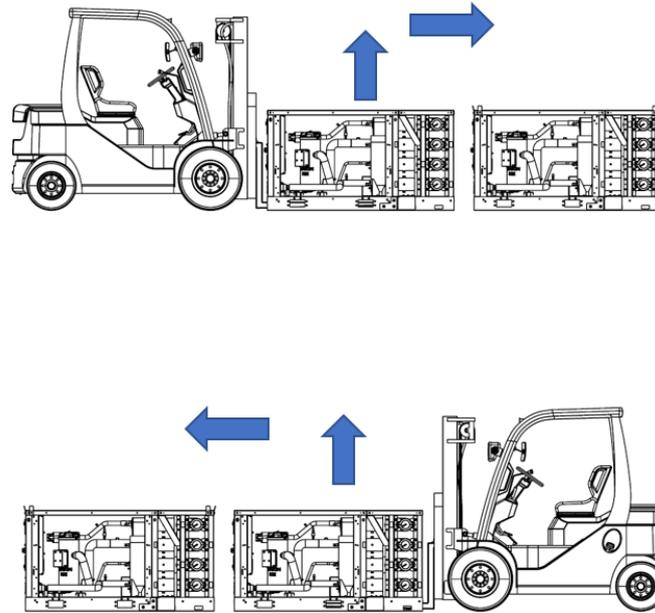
Manipulación del módulo de bombeo con carretilla elevadora
